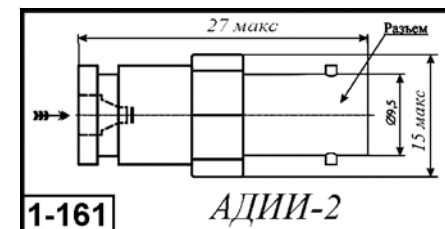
Внешний вид и габаритные размеры детектора АДИИ-2.
